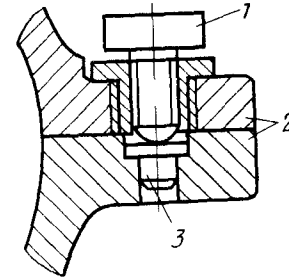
Разжимной винт-съёмник для разборки разъемного корпуса:
